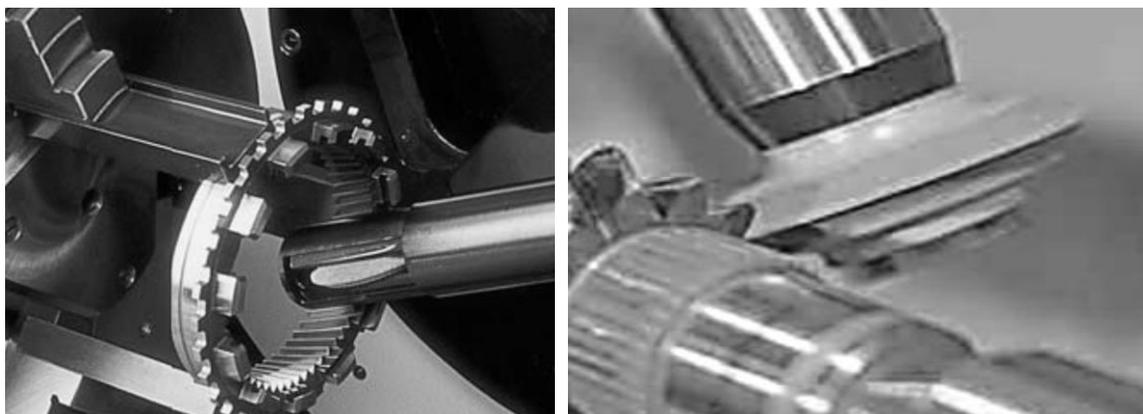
Обработка косозубых эвольвентных колес на станке *SAMPUTENSILI G 500 H
